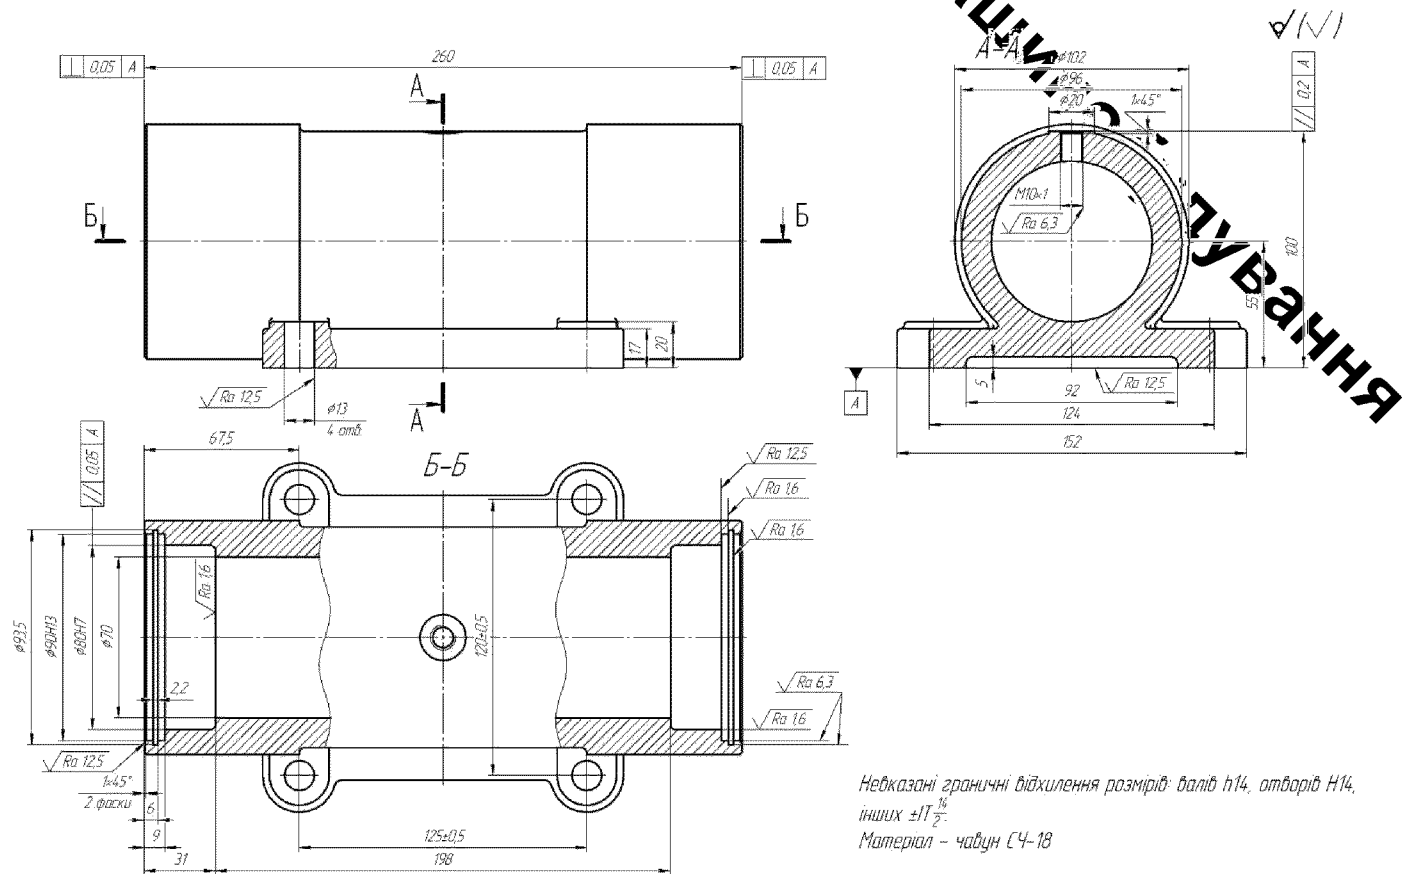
Робоче креслення деталі «Корпус»
